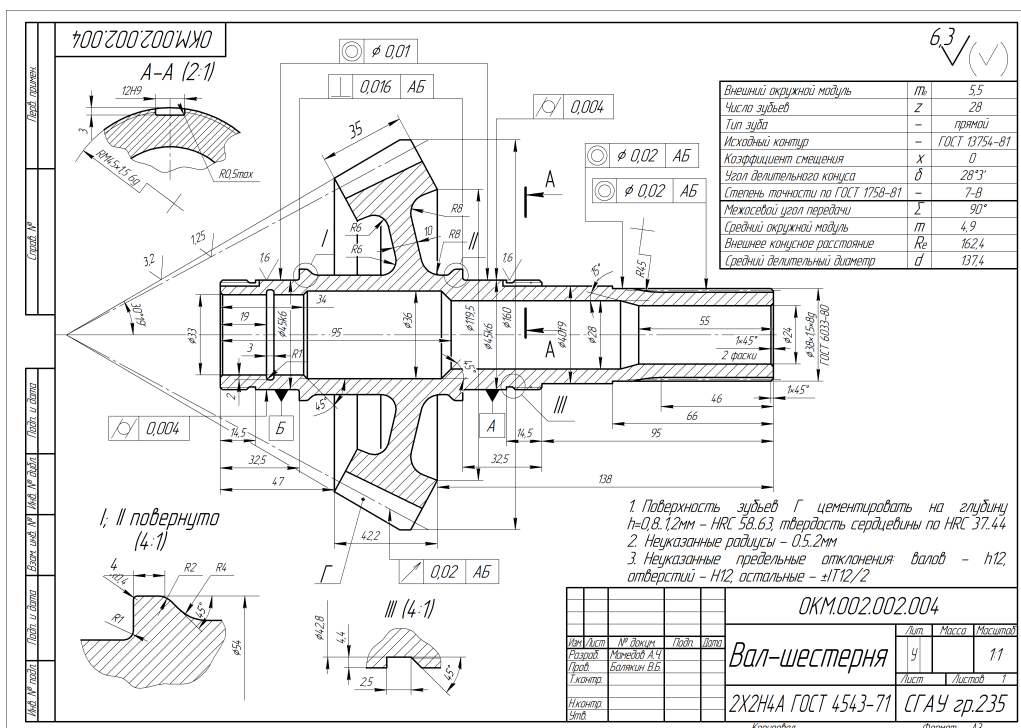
Рабочий чертеж детали, созданный по 3D модели
